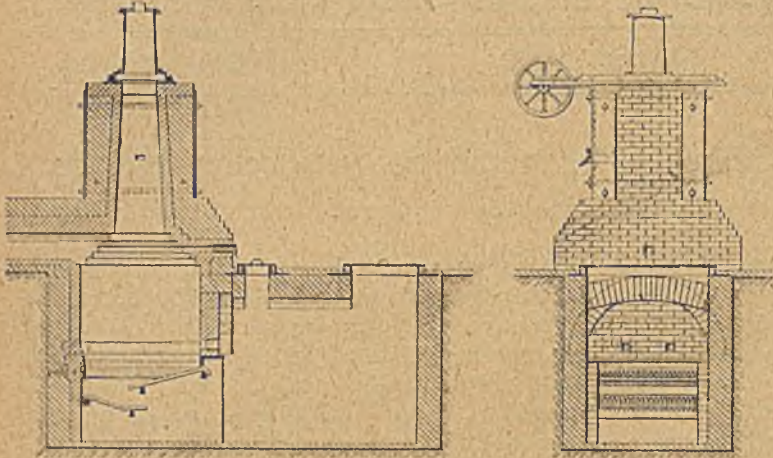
Gaserzeuger zu dem in Abb. 1 dargestellten Schweißofen.
